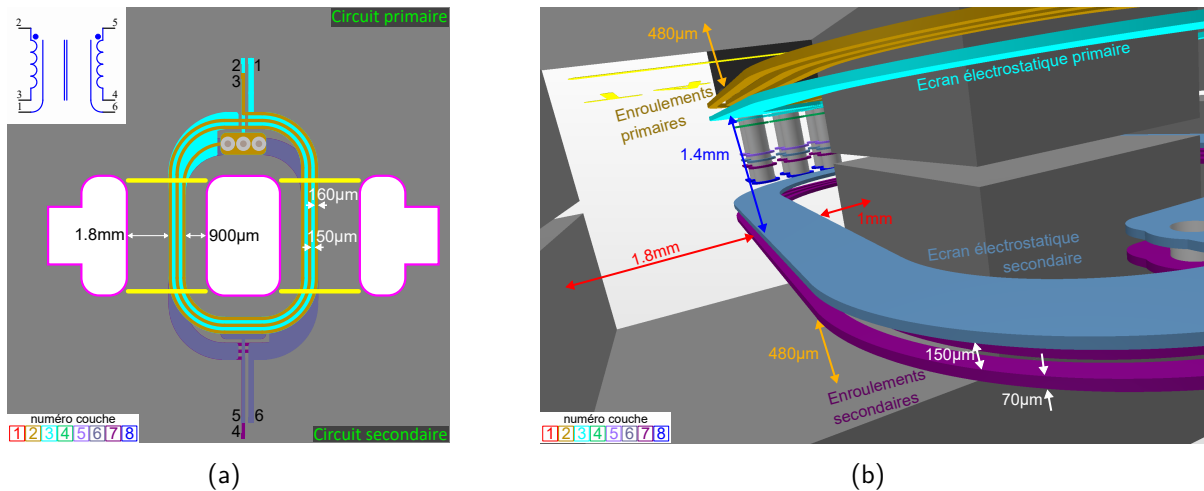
Design du transformateur d'impulsions (a) vue de dessus (b) vue en coupe
